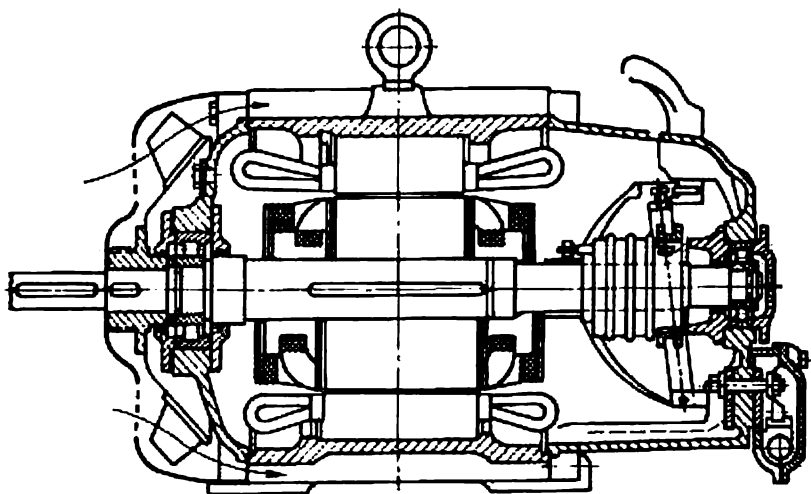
Coupe longitudinale d'un moteur asynchrone à rotor bobiné.
